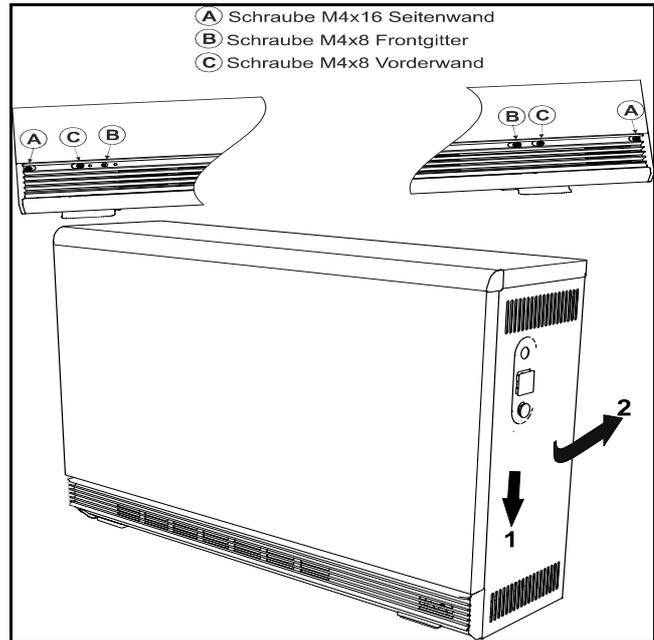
Schrauben der beiden Seitenwände entfernen (A). Die Seitenwände nach unten schieben (1) und ausschwenken (2). Nach Abnehmen der Seitenwände die Befestigungsschrauben (B) des Frontgitters lösen und das Frontgitter entfernen. Danach die Befestigungsschrauben (C) für die Vorderwand lösen.
